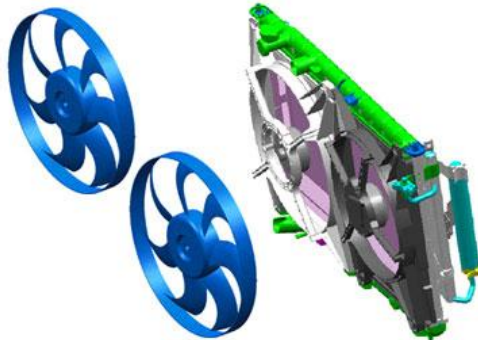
Evaporatör, evaporatör fan motoru, fanlar ve TGV montaj konumları
